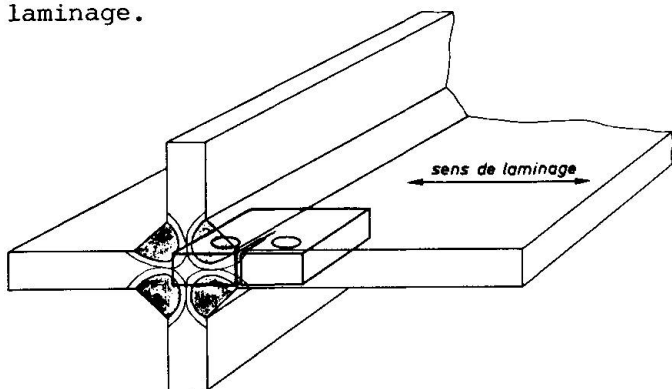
Prélèvement des éprouvettes dans les joints soudés en croix
